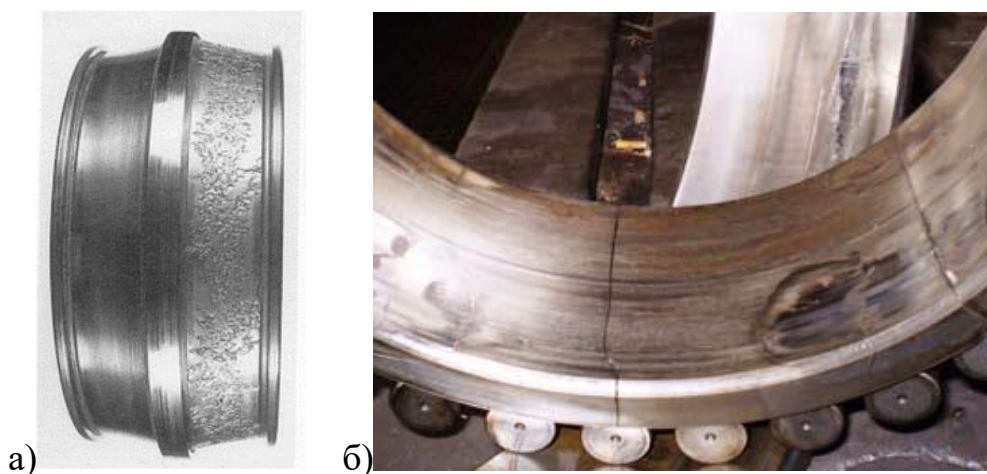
Дефекты подшипников качения: а) выкрашивание поверхности кольца подшипника; б) трещина кольца подшипника
